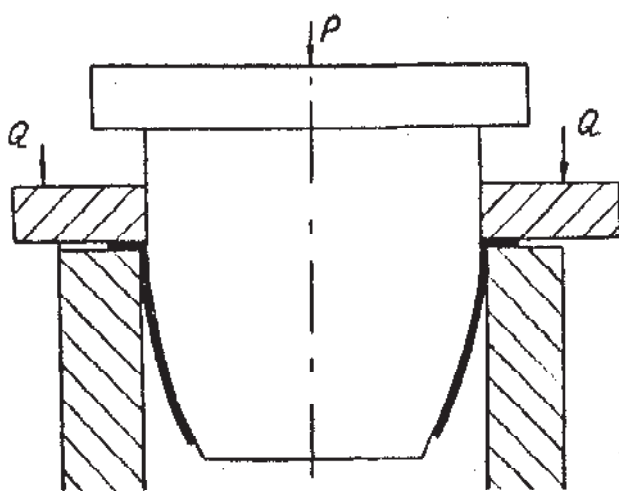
Штамповка в инструментальном штампе тонкостенных заготовок
